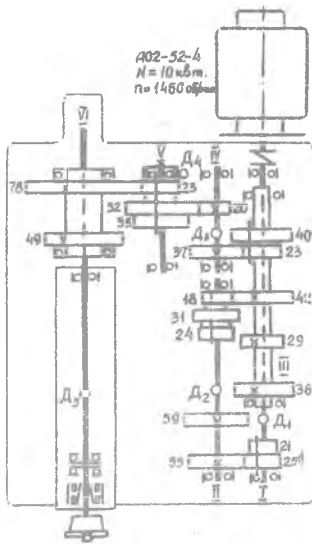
Кинематическая схема привода продольно-фрезерного станка мод. 6606
